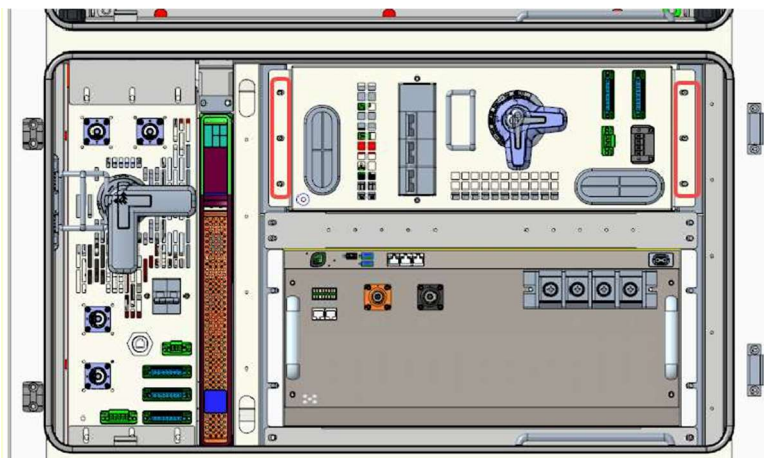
43 Placa protectora frontal del conjunto del disyuntor
